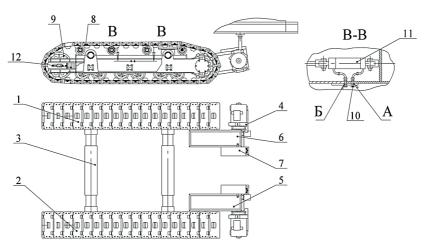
Ход гусеничный бурового станка СБШ-250 МНА-32: 1 и 2 – гусеничные тележки; 4 – электродвигатель; 5 и 6 – редуктор; 7 – тормоз; 8 – лента гусеничная; 9 – натяжное колесо; 10 – крышки; 11 – гидроцилиндр натяжения; 12 – упоры
